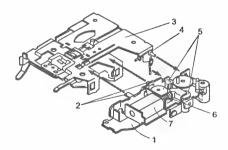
1 — шасси привода механизма микролифта; 2 — направляющие пазы; 3 — кассетоприемник; 4 — пружина привода кассетоприемника; 5 — основные швстерни привода микролифта; 6 — червячная шестерня; 7 — электродвигатель привода механизма микролифта
